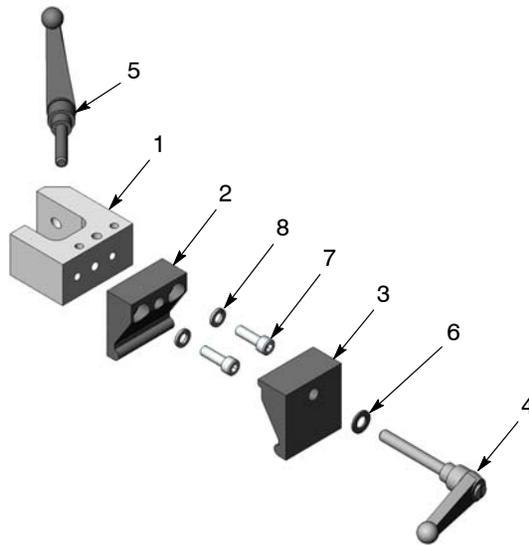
Abrazadera de pistola de montaje en tubo opcional
